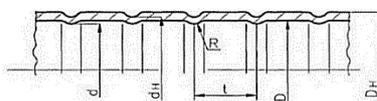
Продольный разрез трубы с кольцевой накаткой
